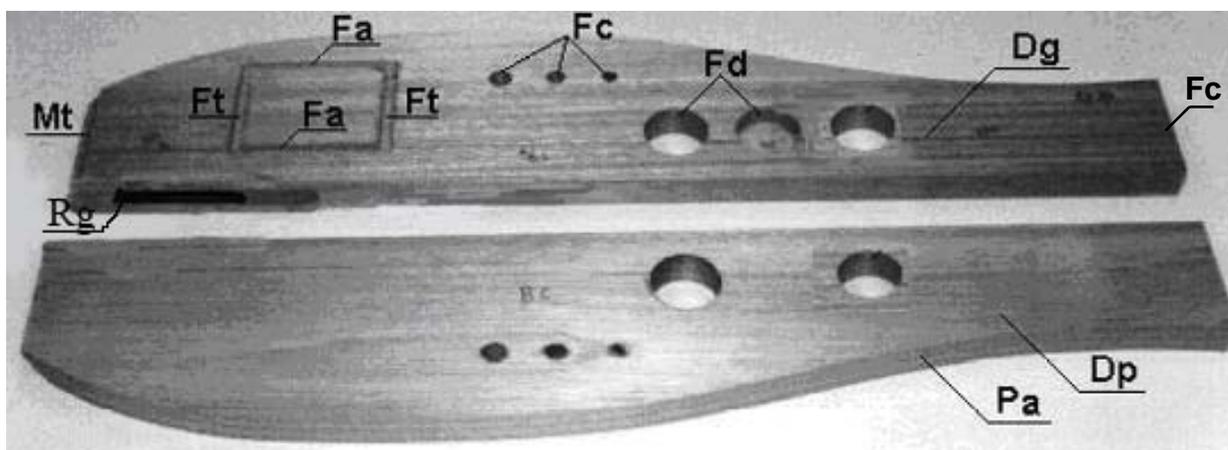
CORPO-DE-PROVA DOS ENSAIOS DE USINAGEM: Dp= desempenho; Dg= desengrosso; Mt= moldura no topo; Pa= perfilagem axial sinuosa (com faca plana); Rg= rasgo na furadeira horizontal; Fa= fresamento axial; Ft= fresamento transversal; Fc= furação para cavilha; Fd= Furação para dobradiça.
